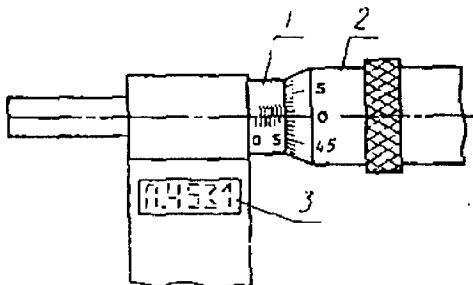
Цифровий показник електронного вимірювального пристрою: 1 — стебло; 2 — барабан; 3 — електронний цифровий вимірювальний пристрій
